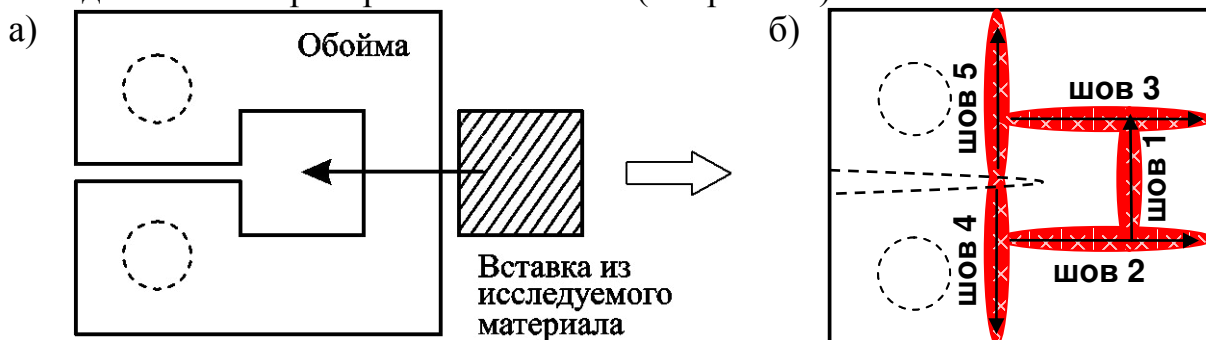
Схема реконструкции образца СТ-0,5 и порядок выполнения сварных швов для одного из оптимальных вариантов.
